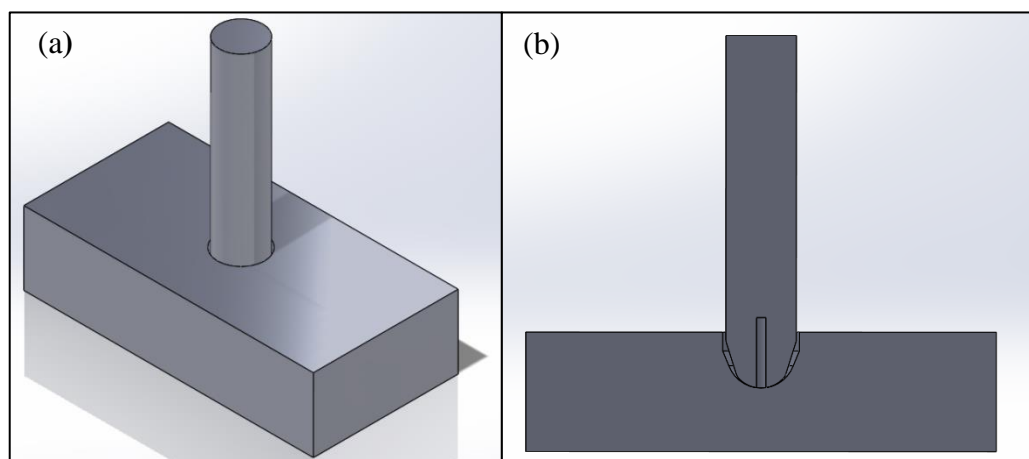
Vista isométrica (a) e vista frontal com corte transversal (b).
